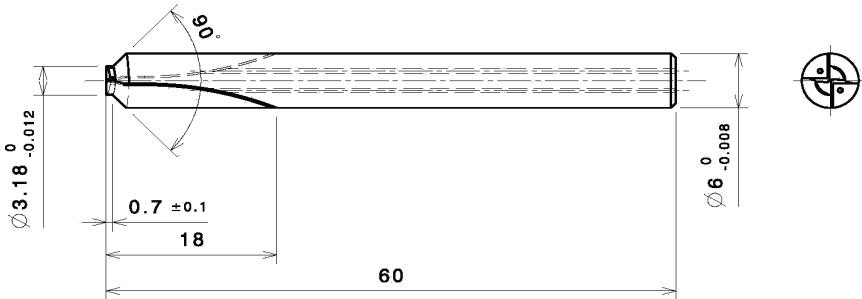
Креслення твердосплавного свердла BOF D3.18X0.7X 60-6 із сплаву UF10
